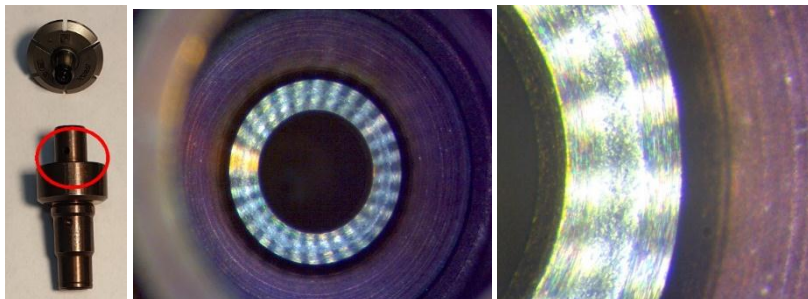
Клапан с запорным пояском корпуса: вид левее 10х, справа 100х
